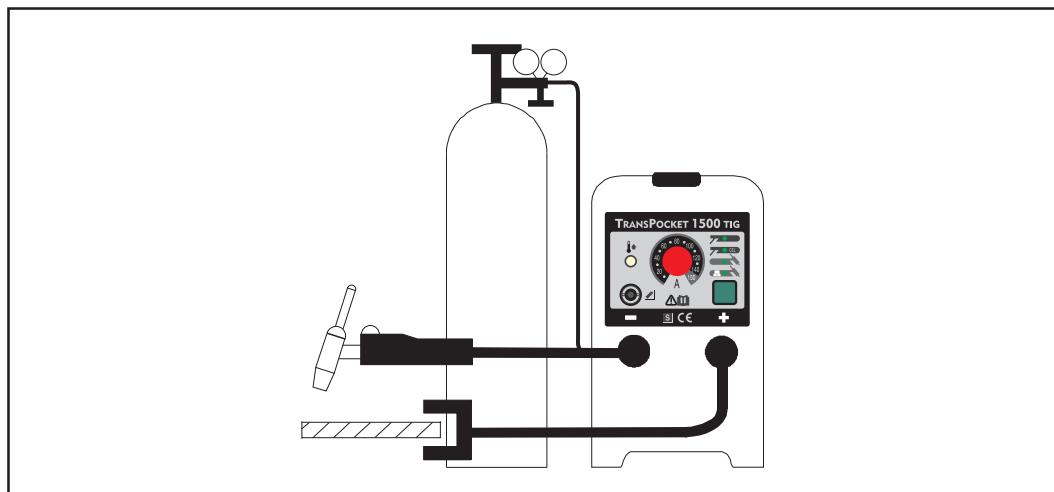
TP 1500 equipado para soldadura TIG
